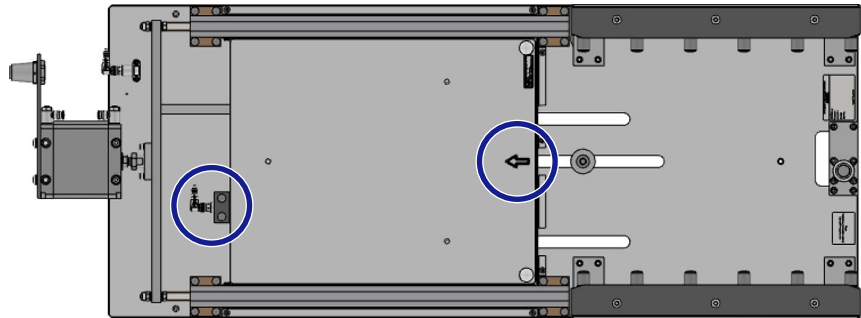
Erreichbare Fixierschrauben (Abbildung beispielhaft)
